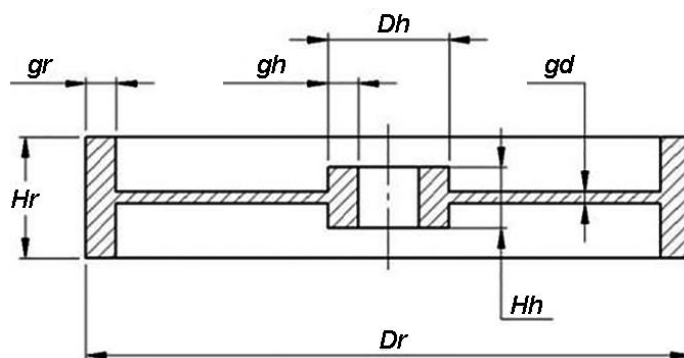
Двухмерный чертеж маховика (вид в разрезе)
